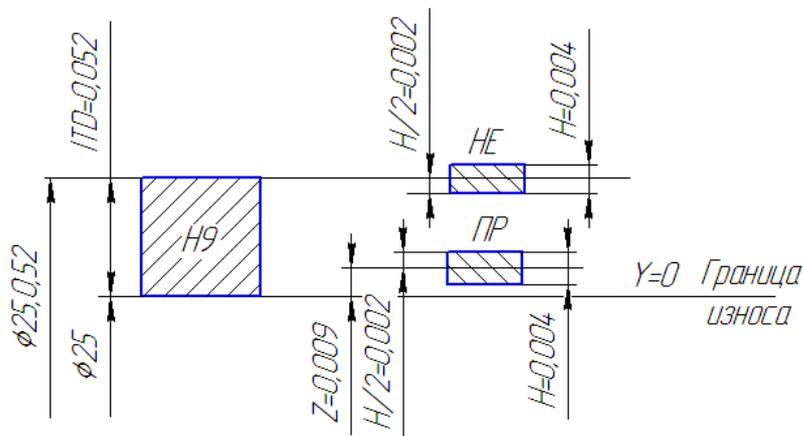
Схемы расположения полей допусков калибра-пробки.
